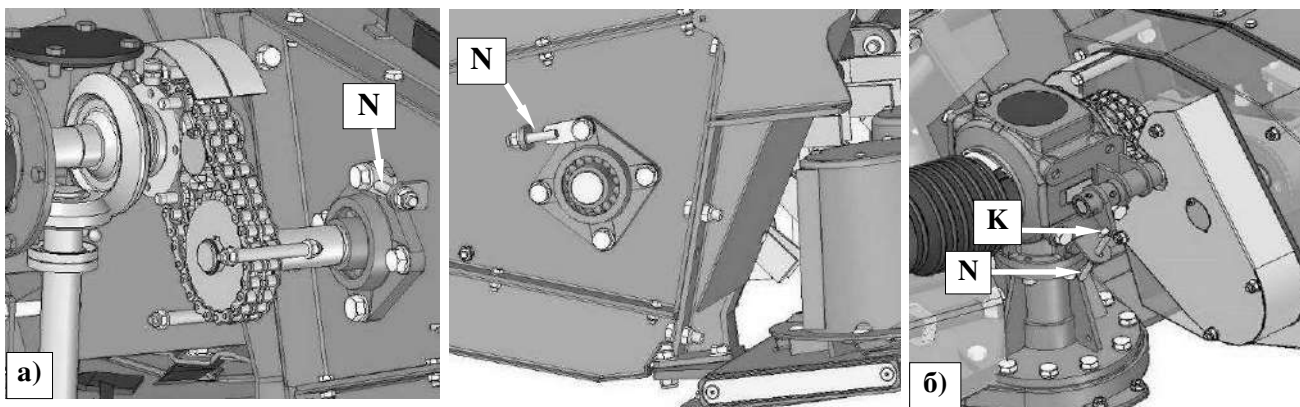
Регулировка напряжения цепи цепной передачи (вид без части предохранителя);
